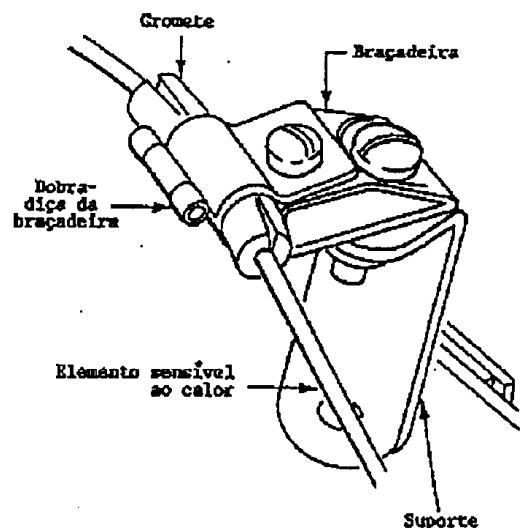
Braçadeira típica de fixação do elemento sensor
